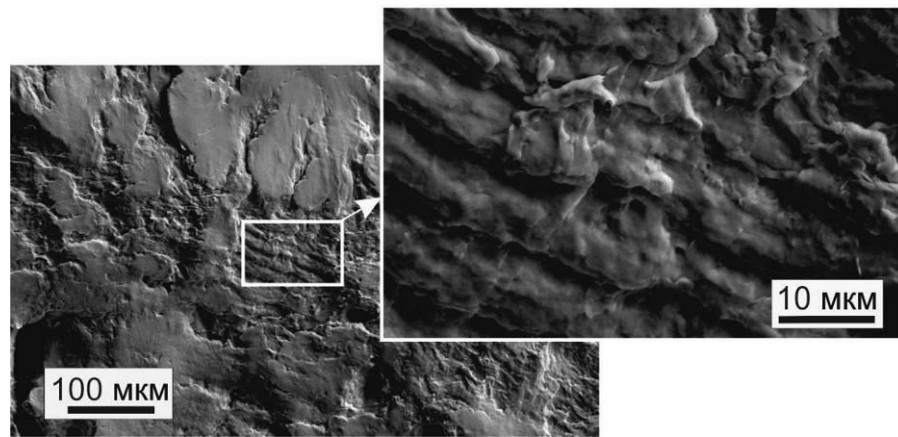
Участки с усталостными бороздками и области со следами пластической деформации на поверхности разрушения образца из стали 45 (закалка с отпуском при 600 °С)
